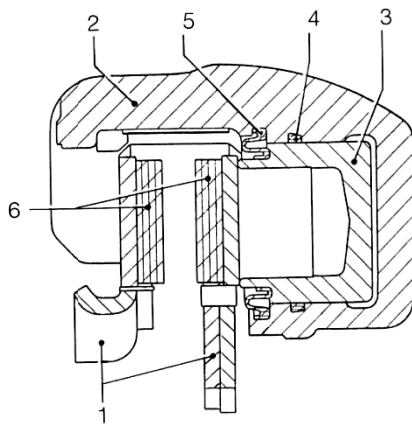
Детали стандартного, однопоршневого тормозного суппорта:
